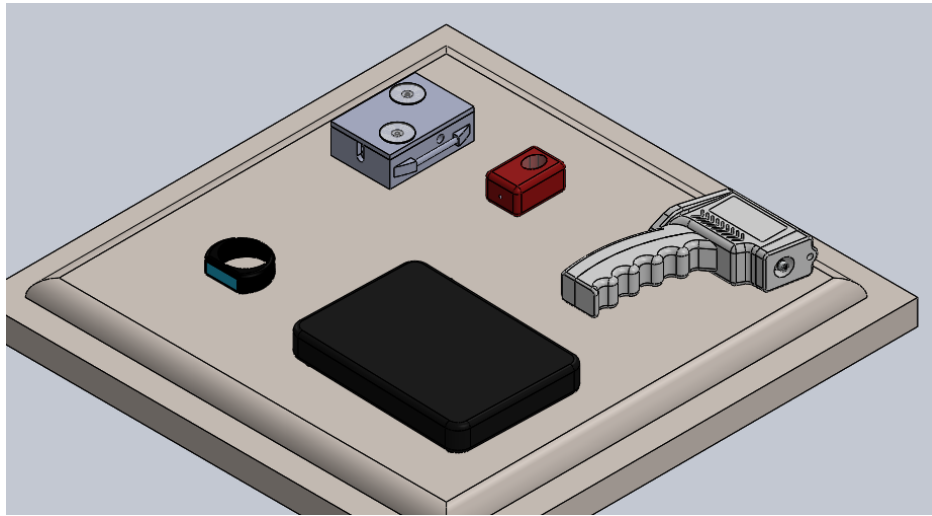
Imagen del diseño CAD de la Caja de control del sistema. [autores]
